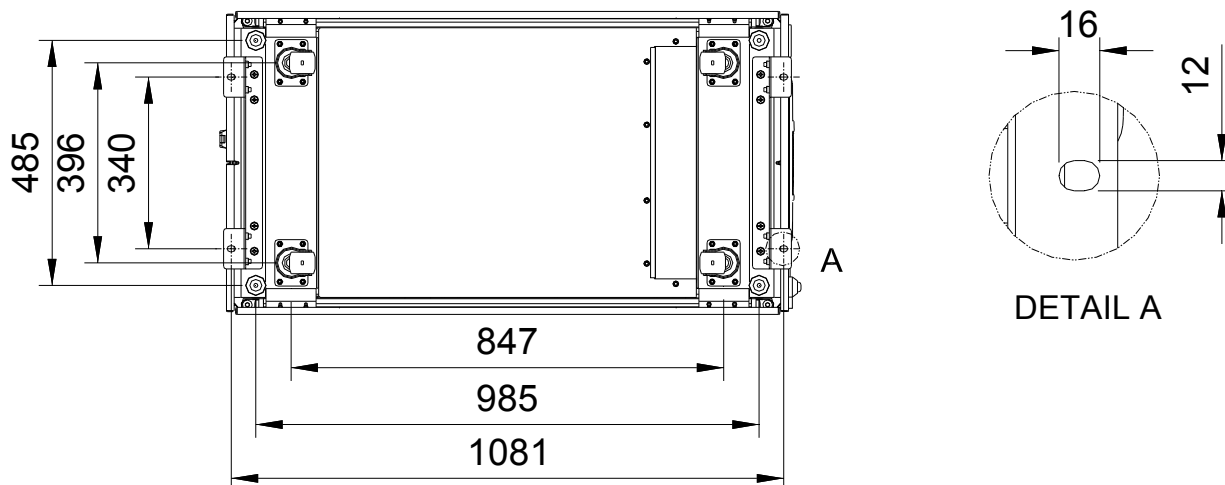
Вид ИБП и батарейного шкафа снизу; показано положение роликов и крепежных отверстий
